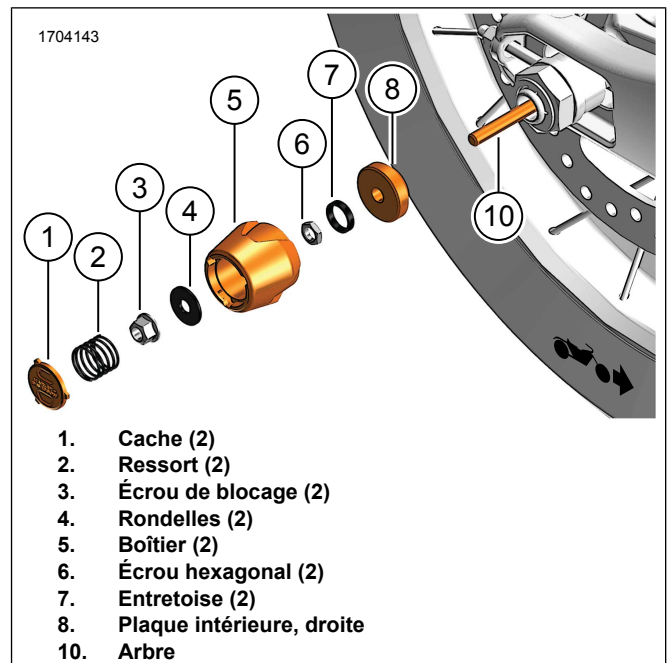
Ensemble de couvercle d'essieu arrière (côté droit illustré)
